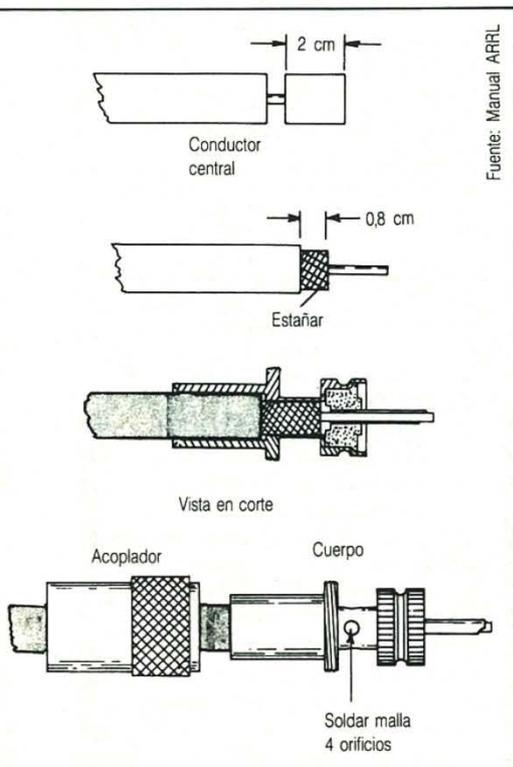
Forma que suele recomendarse para soldar el conector PL-259.
